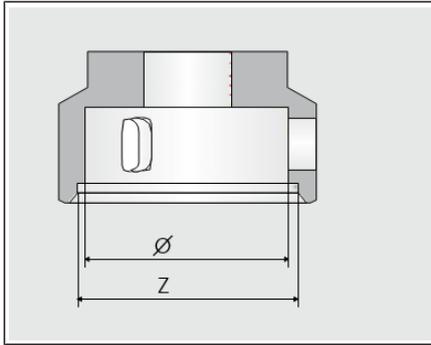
Expulsor de produto \varnothing = Diâmetro de tração Z = Pré-centragem
